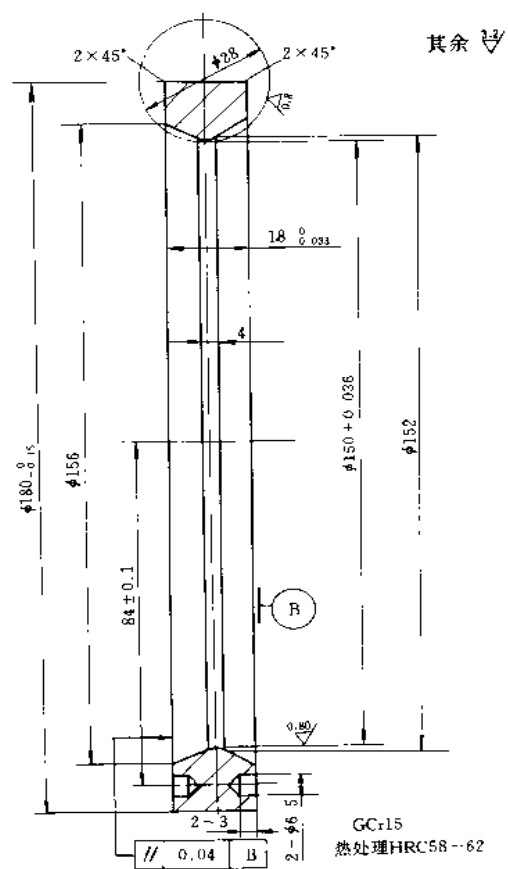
行星弧锥无级变速器的典型零件图 (a)
